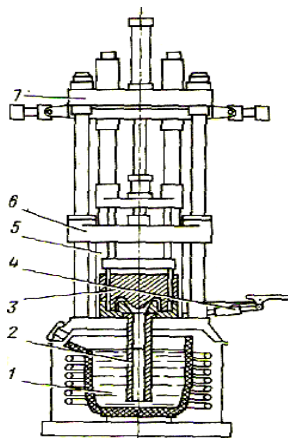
Схема машины литья с противодавлением типа ВП:1- герметичная печь с расплавом; 2 - металлопровод; 3 -форма; 4 - съемник отливок; 5 - герметичный кожух; 6-подвижная плита машины; 7 - механизм вертикальных перемещений.
